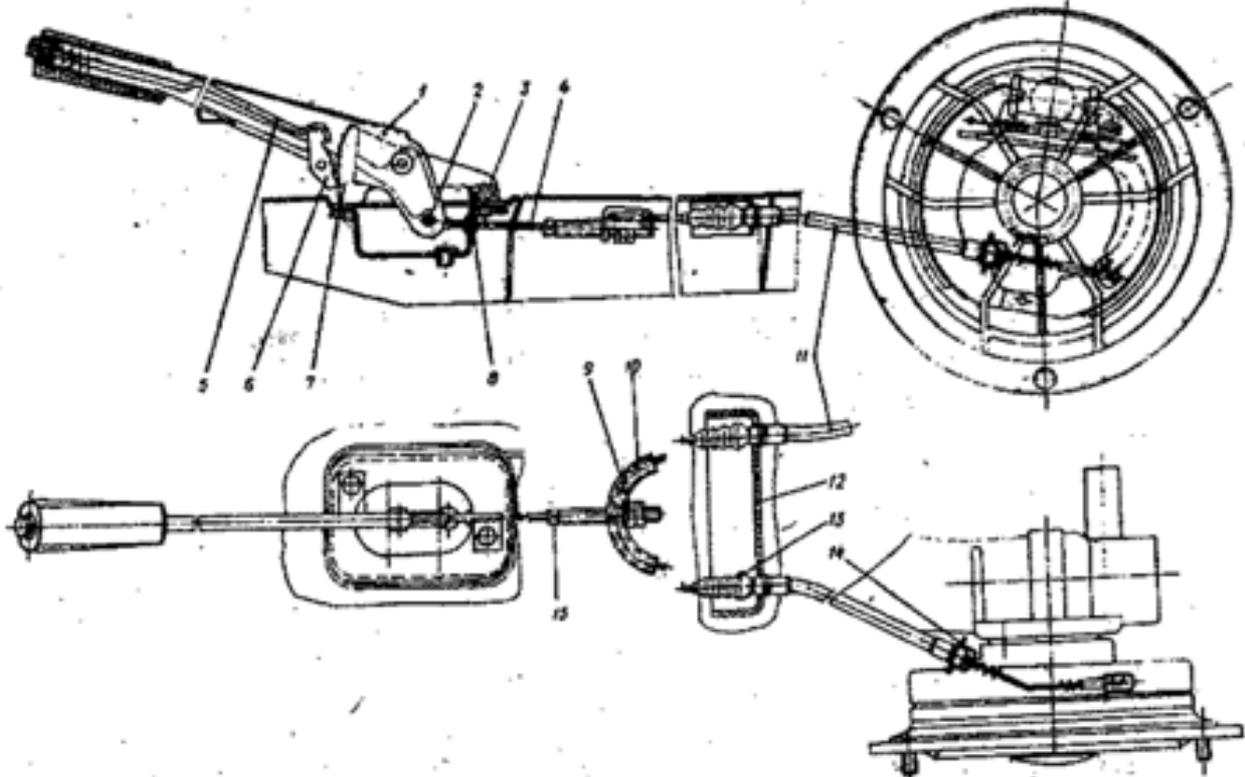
Стояночный тормоз и его установка на автомобиль: 1 - рычаг; 2 - палец; 3 - болт крепления; 4 - трос передний; 5 - стержень; 6 - собачка; 7 - сектор; 8 - уплотнитель; 9 - гайка регулировочная; 10 - уравниватель троса; 11 - трос привода стояночного тормоза; 12 - кронштейн; 13 - уплотнитель троса; 14 - упор; 15 - квадрат на наконечнике переднего троса.
